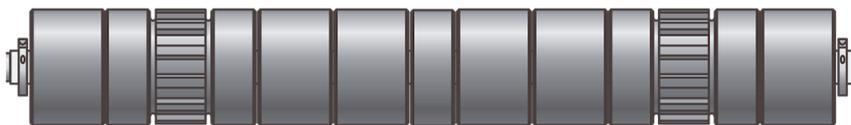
Engranaje apilado/rueda de soporte (engranaje cuadrado de 6 pulg. de ancho)
